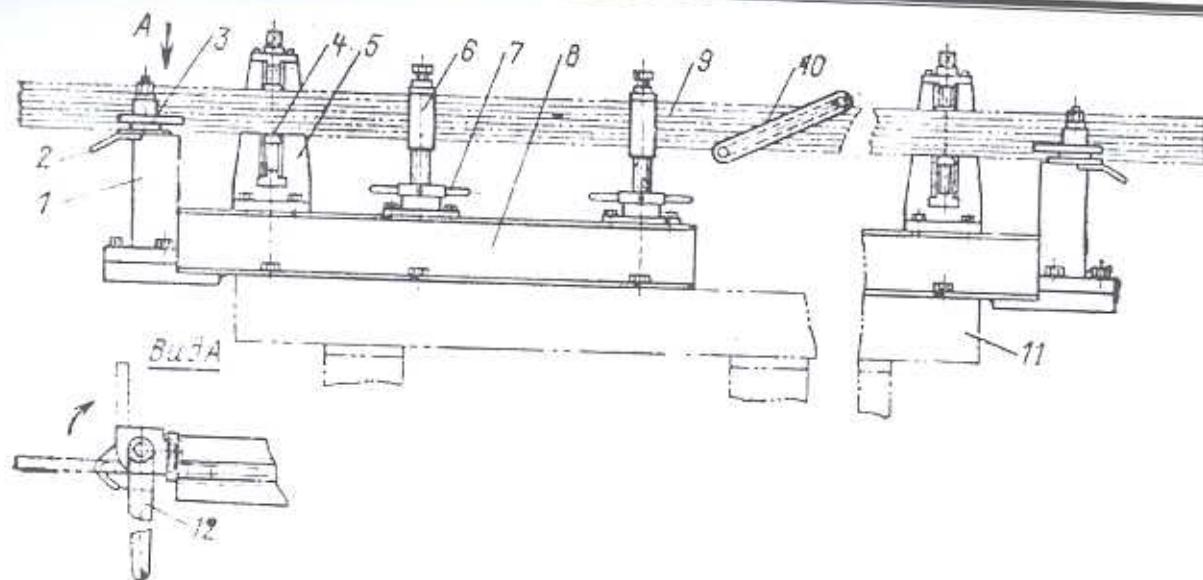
Приспособление для гибки полувитков в сборе:
